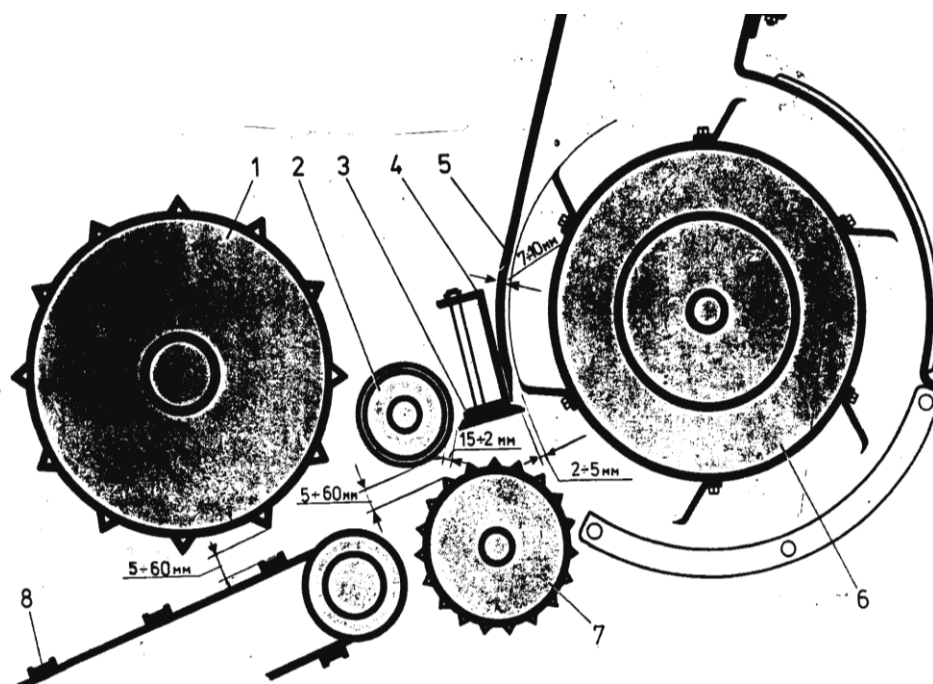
Зазор между рабочими органами питающего устройства: 1 – питающий барабан; 2 – гладкий валец; 3 – противорезущая пластина; 4 – брус крепления противорезущей пластин; 5 – лобовой лист; 6 – измельчающий барабан; 7 – нижний битерный барабан; 8 – транспортер жатки
